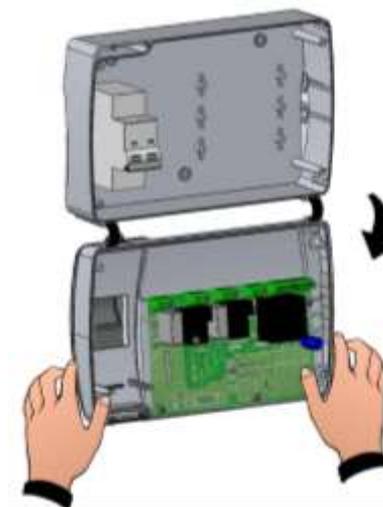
Üben Sie einen Druck auf jede der einzelnen Scharniere aus, um sie aus ihrem Sitz zu lösen und entfernen Sie die gesamte Front.
